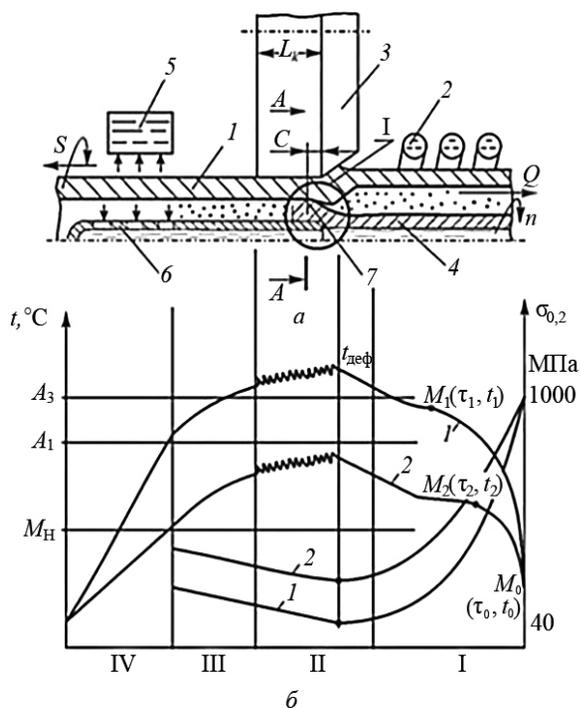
Схема ВТМО ВО труб на оправке (а) и кривые изменения температуры заготовки, определяющие вид обработки по классификации М.Л. Бернштейна (б): а) 1 — заготовка; 2 — индуктор; 3 — оправка; 4 — три неприводных ролика; 5, 6 — наружный и внутренний спрейеры; б)  $M_0$  — начальная температура заготовки;  $M_{1,2}$  — температура и время нагрева ТВЧ; I — нагрев; II — деформация; III — последеформационная выдержка; IV — охлаждение
